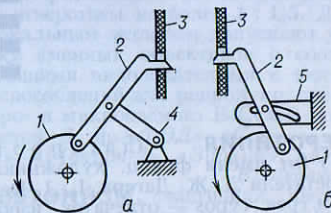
Схемы кривошипных рейферных механизмов: а — с балансиром; б — с неподвижной направляющей; 1 — кривошип; 2 — рейфер; 3 — киноплёнка; 4 — балансиры; 5 — неподвижная направляющая.
